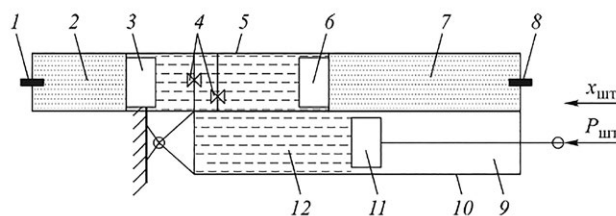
Конструктивная схема ДУ ГПР: 1, 8 – зарядный клапан; 2, 7 – пневматическая полость; 3, 6 – поршень-разделитель; 4 – дросселирующая система; 5 – пневмоцилиндры; 9 – штоковая полость гидроцилиндра; 10 – гидроцилиндр; 11 – поршень со штоком; 12 – поршневая полость гидроцилиндра; $X_{шт}$ – направление перемещения штока при прямом ходе подвески; $P_{шт}$ – направление действия силы.
